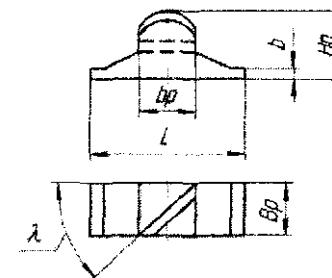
Конструкция вставного резца-зуба развёртки
